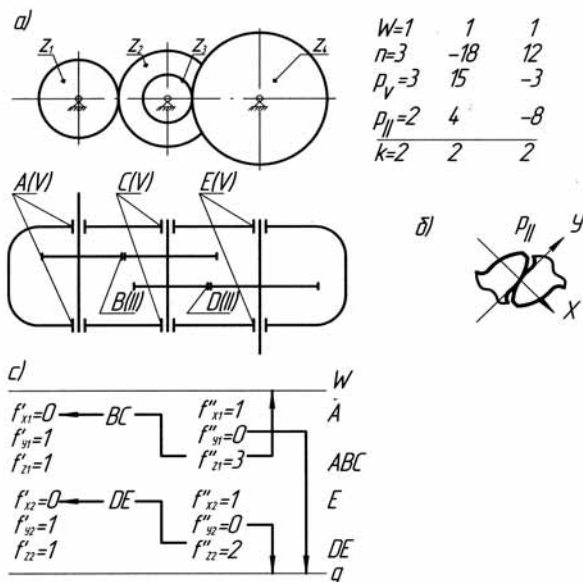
Применяемый редуктор: а – кинематическая схема; б – контакт зубьев первой ступени редуктора; с – таблица распределения подвижностей в кинематических парах
